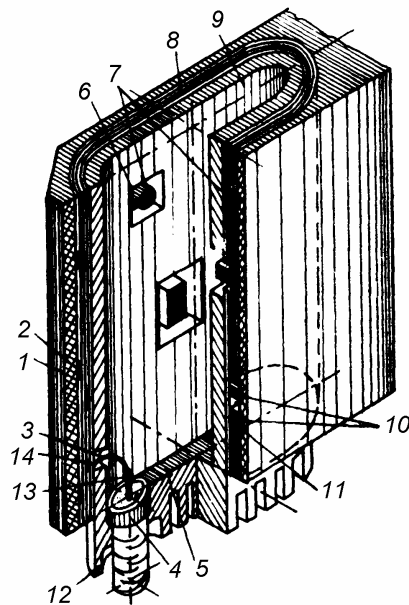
Конструкция модуля МФ ОИС с послойной навивкой полиимидной ленты: 1 — корпус из пеноматериала; 2 — ПЭ; 3 — соединительный проводник; 4 — СВЧ-соединитель; 5 — радиатор; 6 — отверстие под установку НЭ; 7 — НЭ; 8 — композиционная лента; 9 — основание-оправка; 10 — НЭ малой мощности; 11 — отверстие в навитой композиционной ленте; 12 — зона установки СВЧ-соединителя; 13 — центральный проводник СВЧ-соединителя; 14 — пайка
